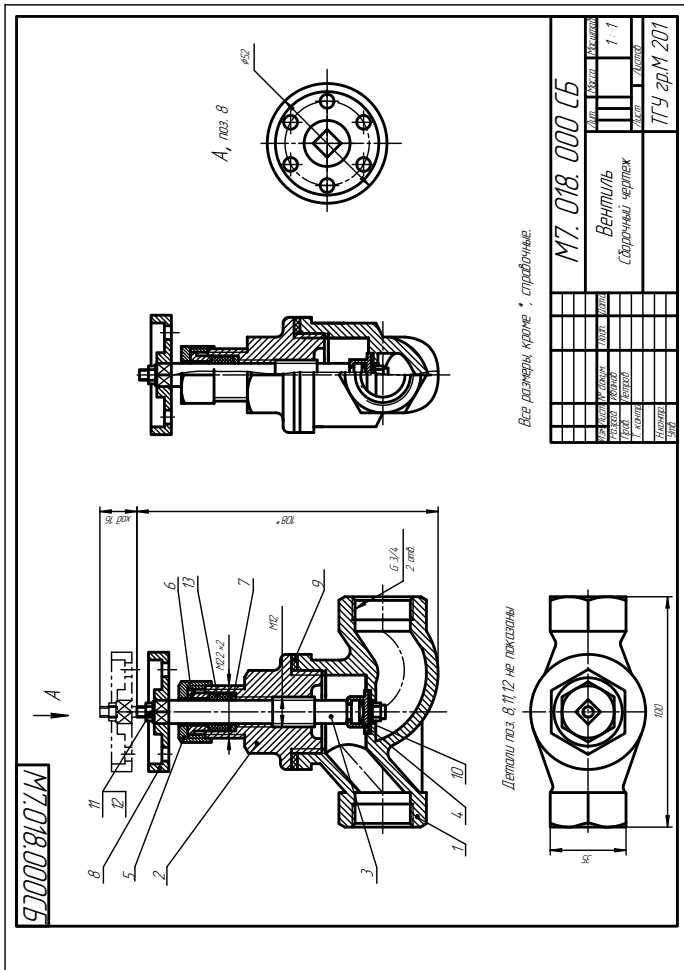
Сборочный чертёж вентиля с корпусом сложной формы
